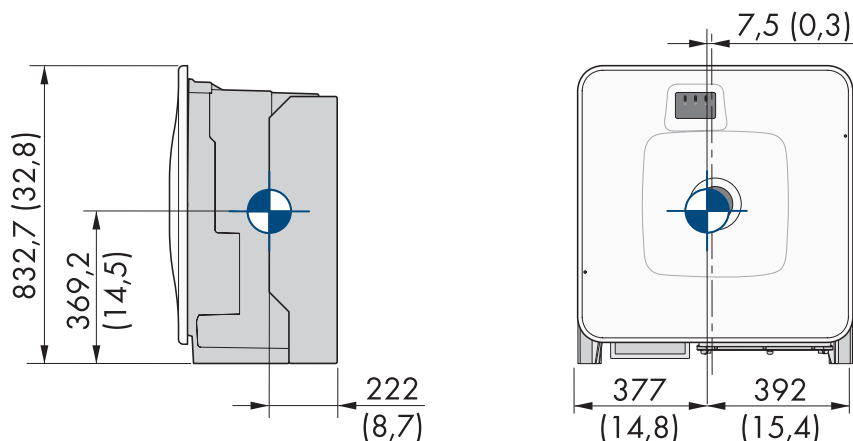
Dimension du centre de gravité du produit (mesures en mm (in))
